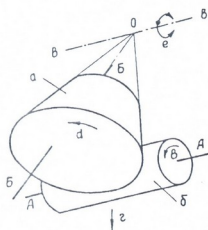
Схема нарезания некруглого конического колеса цилиндрической червячной фрезой
